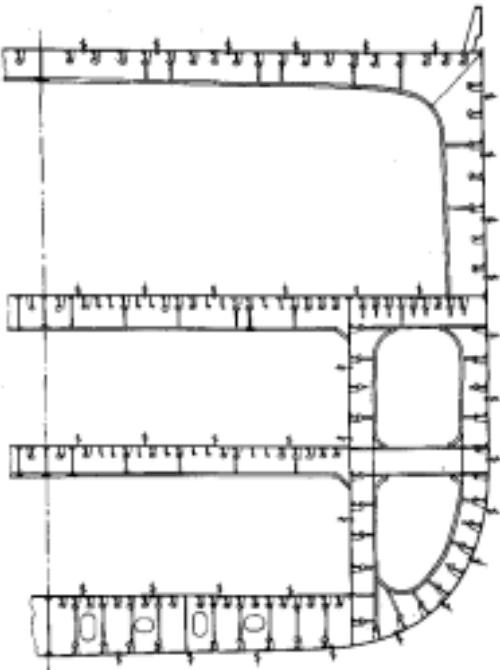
Поперечное сечение наклонного двухпалубного судна без палубных вырезов
